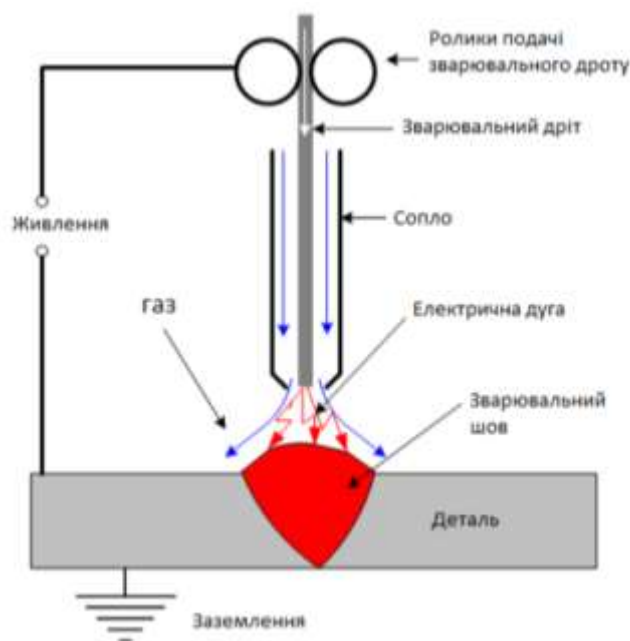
Схема напівавтоматичного зварювання у вуглекислому газі
